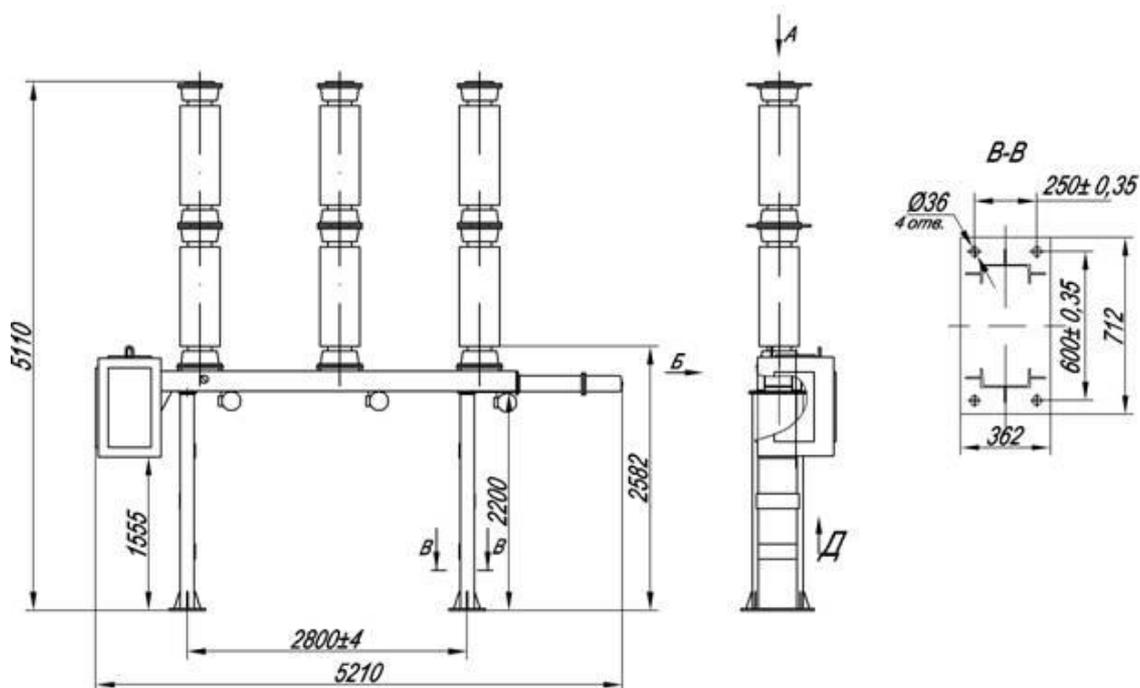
Внешний вид выключателя ВГТ – 110
